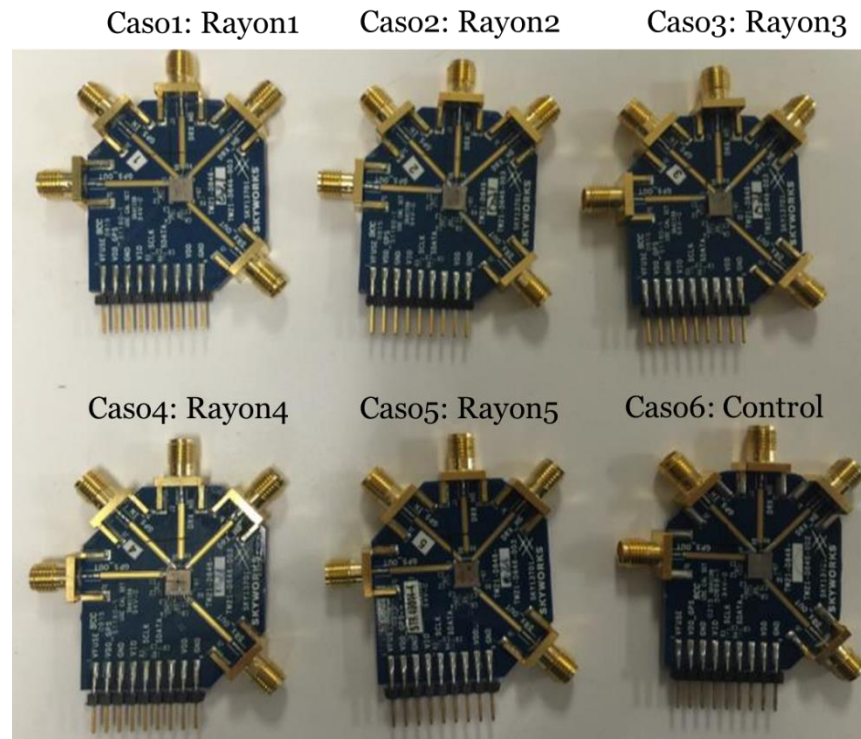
Muestras instaladas en tableros para prueba bench
